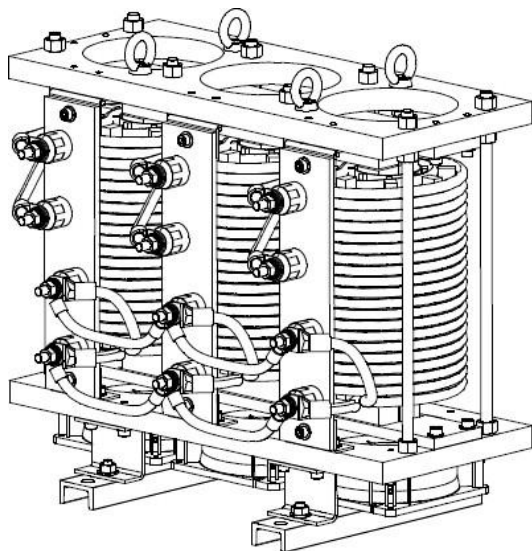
3D-креслення 3-фазного СЧТ
